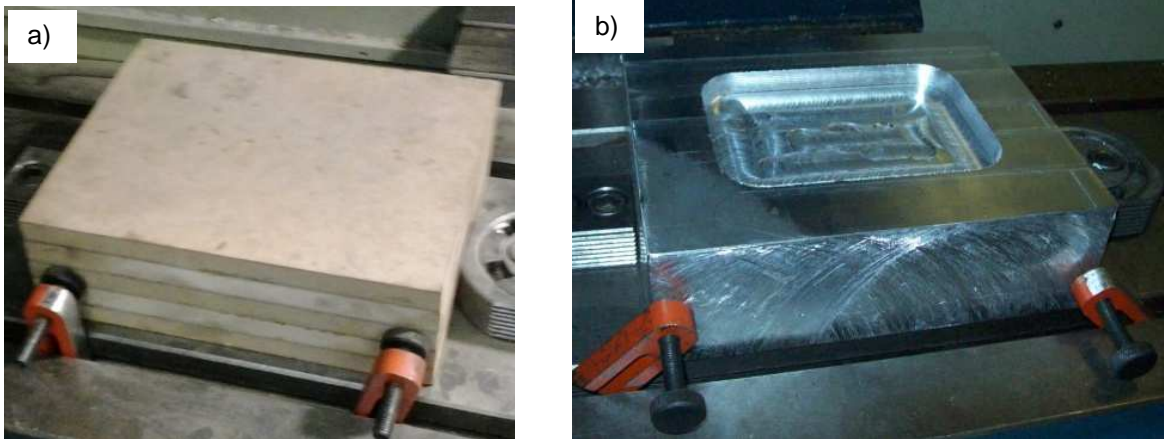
a) Bloco de MDF utilizado para fabricação do molde; b) Bloco de alumínio utilizado para fabricação do molde.
